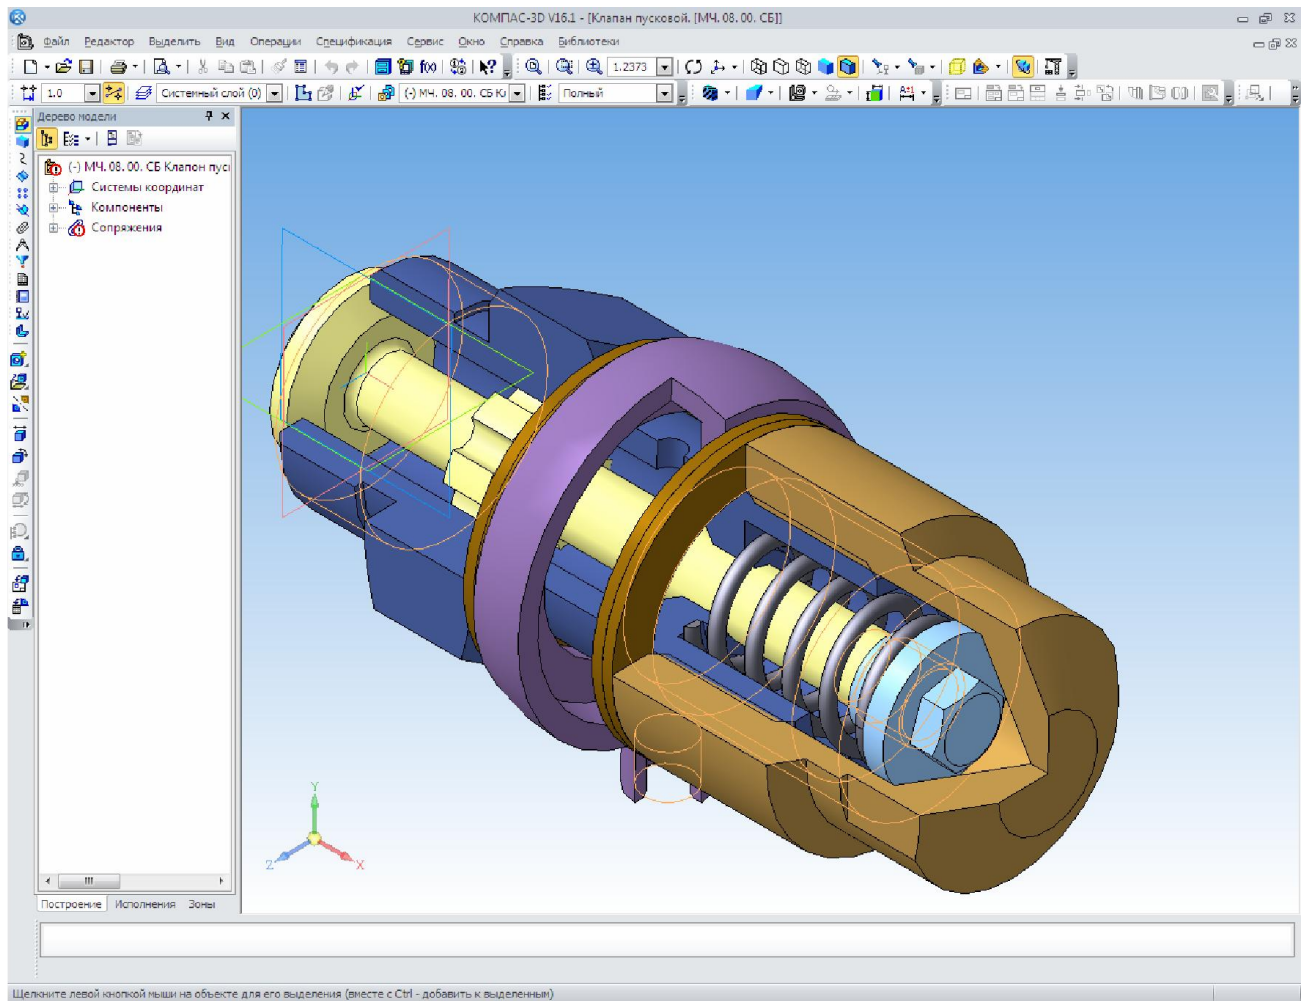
Клапан пусковой, 3D сборка – общий вид
